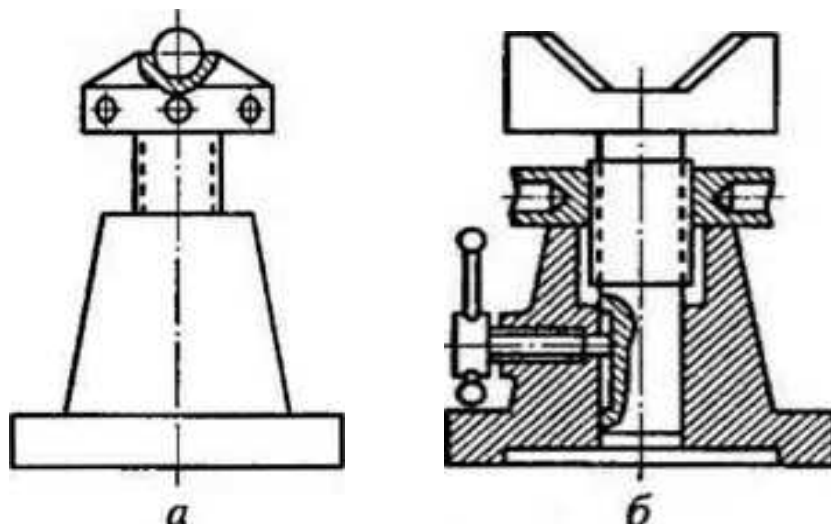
Домкраты с шаровой (а), призматической (б) опорой для заготовки
